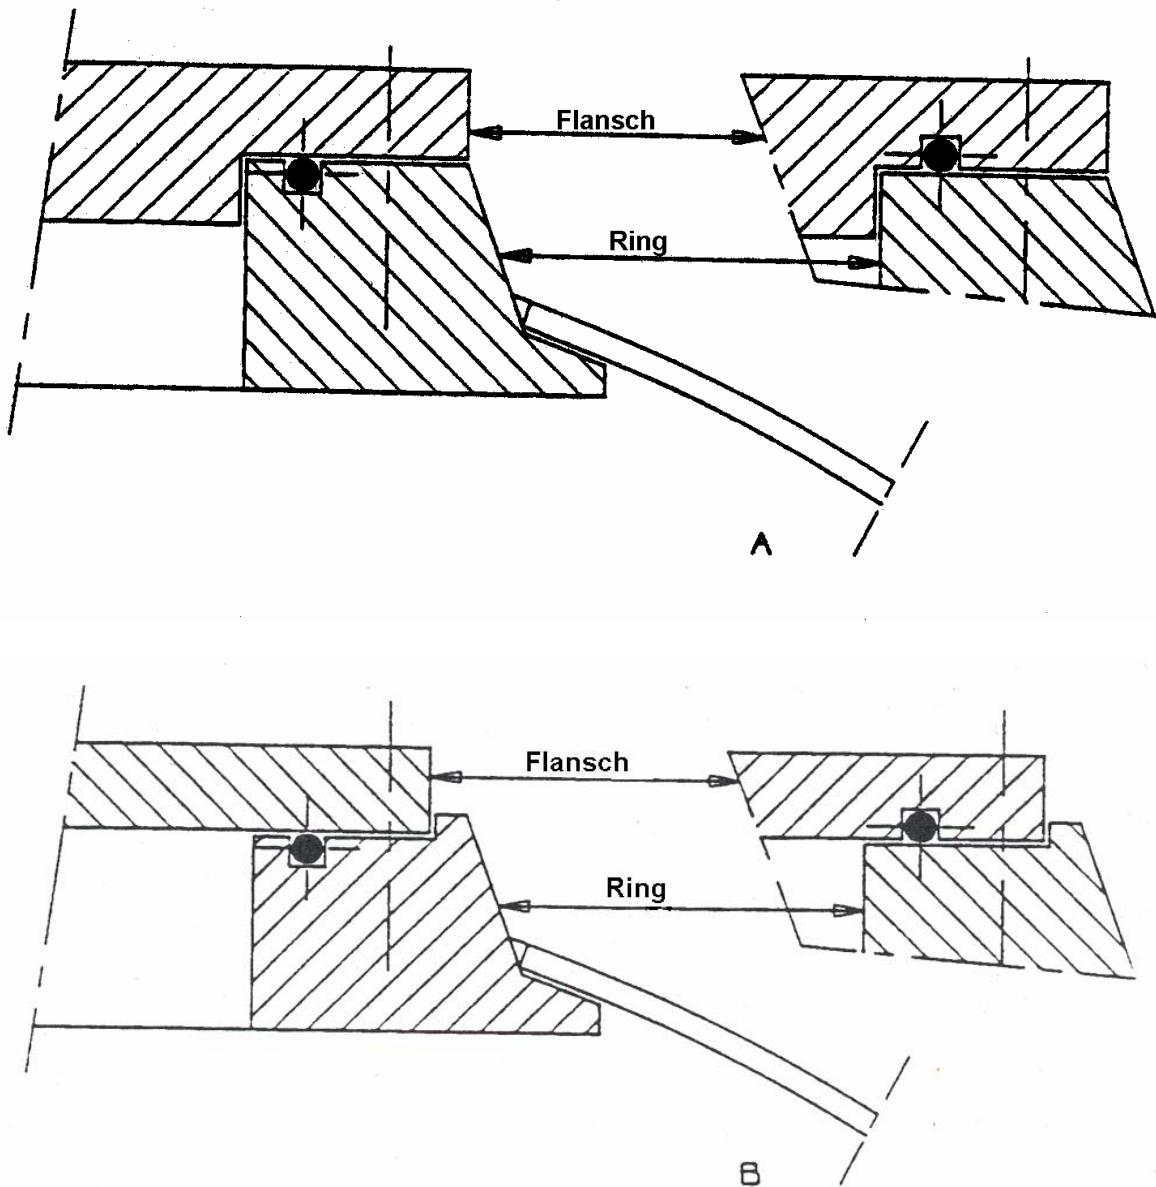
Beispiele für geschweißte Ringe mit Flansche
